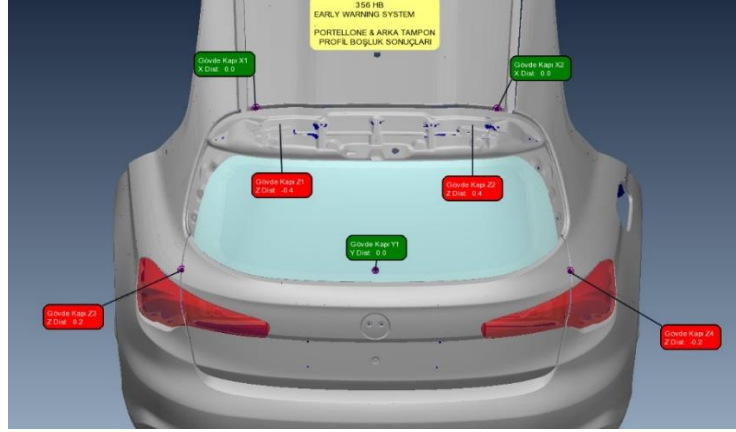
22. Egea Hatchback Bagaj kapağı single projesi
